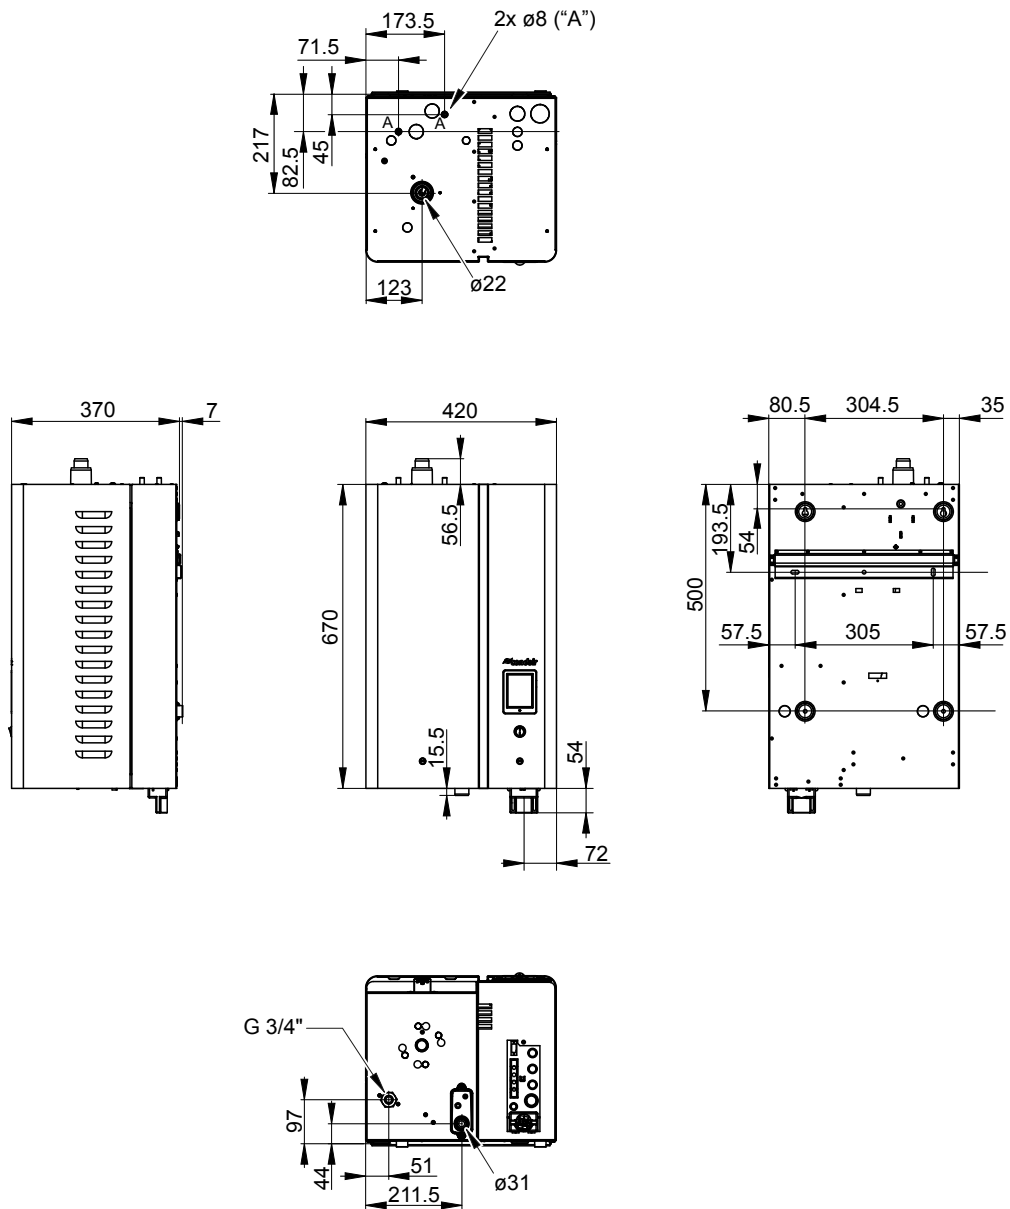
Figura de dimensiones Condair EL 5 - 15, tamaño de la carcasa "S" (dimensiones en mm)
